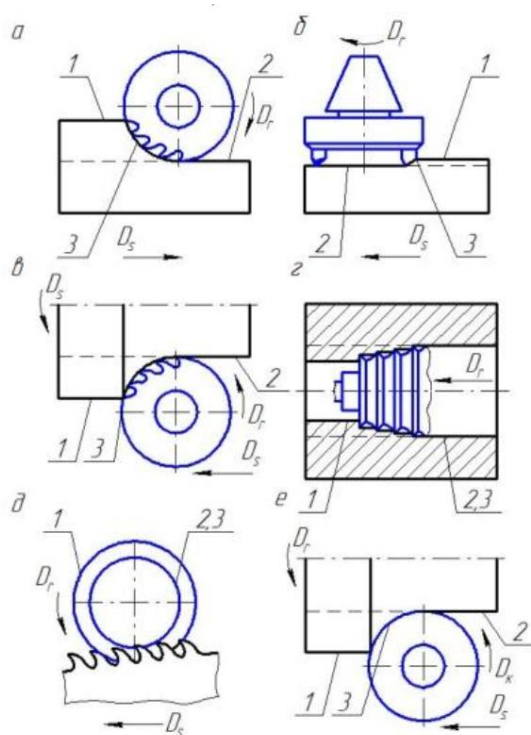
Схемы видов лезвийной обработки: а - периферийное (цилиндрическое, дисковое и т.п.) фрезерование; б - торцовое фрезерование; в - круговое фрезерование; г - внутреннее протягивание; д - наружное протягивание; е - ротационное точение. 1 - обрабатываемая поверхность; 2 - обработанная поверхность; 3 - поверхность резания;  $D_r$  - главное движение;  $D_s$  - движение подачи;  $D_k$  - касательное движение.
